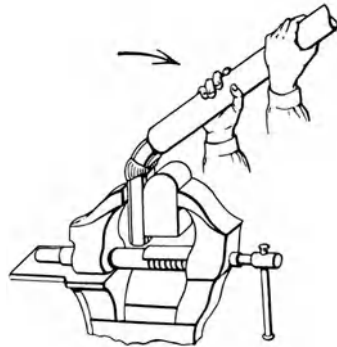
Schraubstockbiegeprobe für Schweißnähte.
